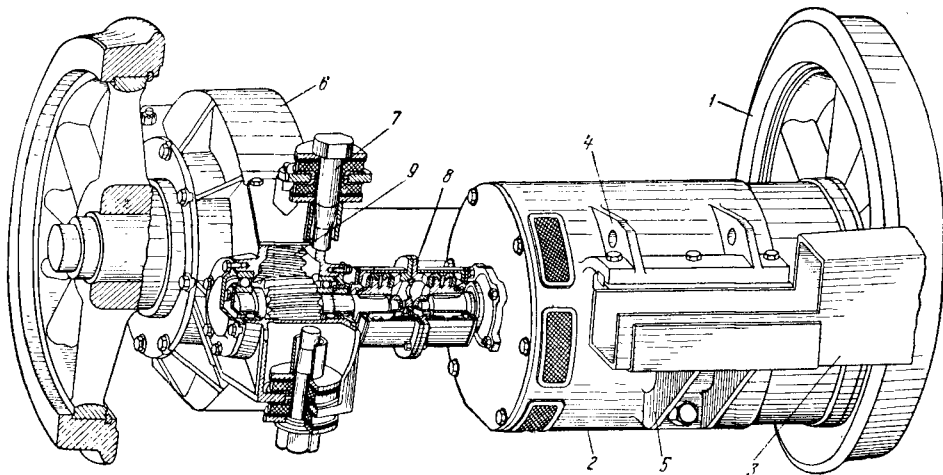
Эластичный привод с дисками в сборе с колёсной парой и тяговым двигателем: 1—втулка поводка; 2—диск привода ведущей стороны; 3—поводок вала привода; 4—вал привода; 5—поводок вала привода с ведомой стороны; 6—диск привода с ведомой стороны; 7—поводок вала хвостовика шестерни; 8—зубчатки; 9—кожух передачи; 10—качающаяся подвеска кожуха зубчаток
